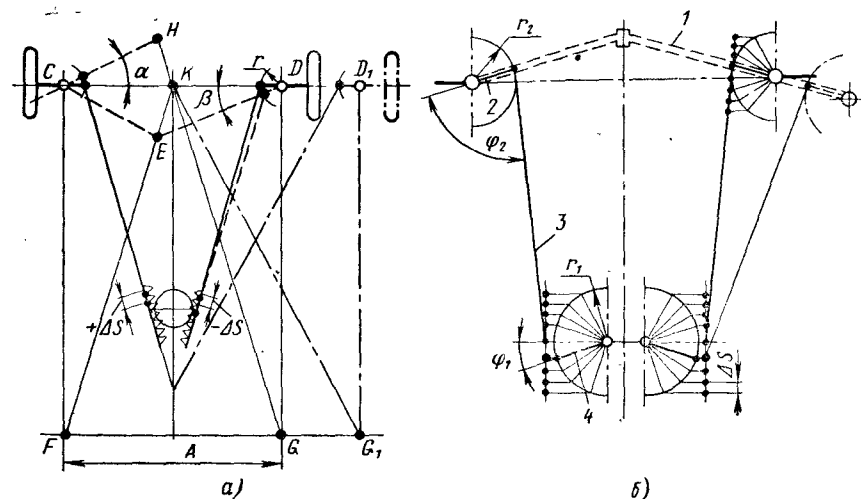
Схемы приводов с двумя продольными рулевыми тягами: а — тяги параллельны сторонам базового треугольника; б — тяги образуют с рычагами острый угол; 1 — передняя ось; 2 — поворотный рычаг; 3 — продольная тяга; 4 — сошка (условно повернута из вертикальной плоскости в горизонтальную)
